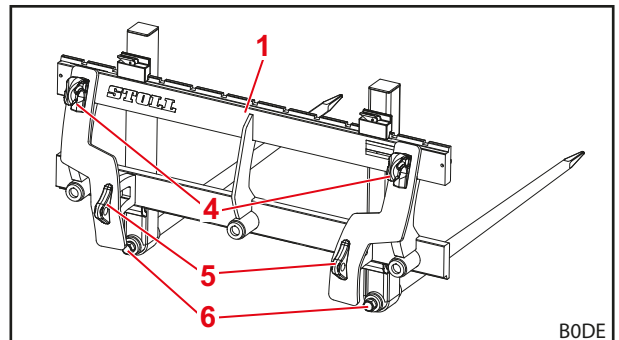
Конструкция вилок для крупных тюков HS – вид сзади (пример: со стандартными зубьями)
